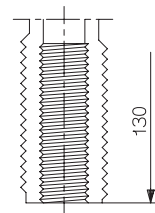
Gewindebohrer M8x0,75 Typ 1361
